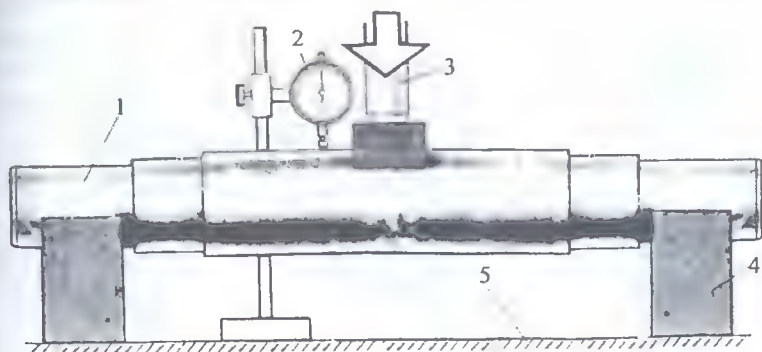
Исправление прогиба вала: 1 — вал; 2 — индикатор; 3 — шток пресса; 4 — призма; 5 — стол пресса
